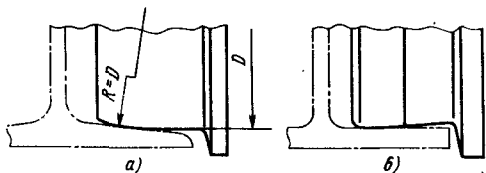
Профили беговых поверхностей колес подвесных тележек:
